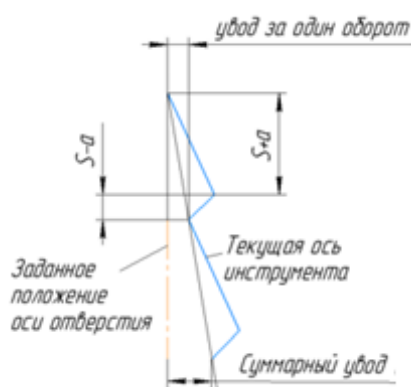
влияние осевых колебаний шпинделя станка на увод оси отверстия
